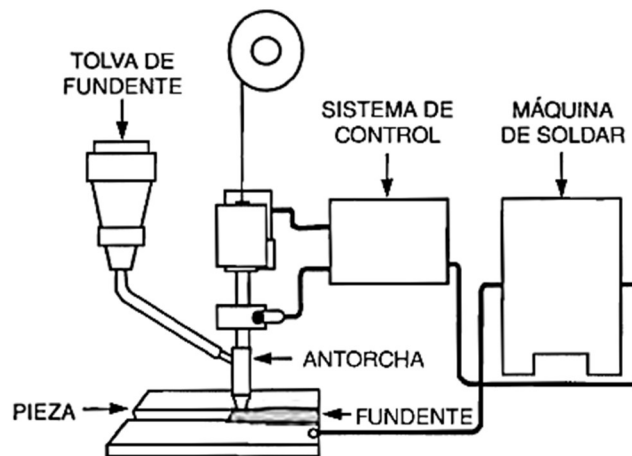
Equipo para soldadura por arco sumergido (3).
